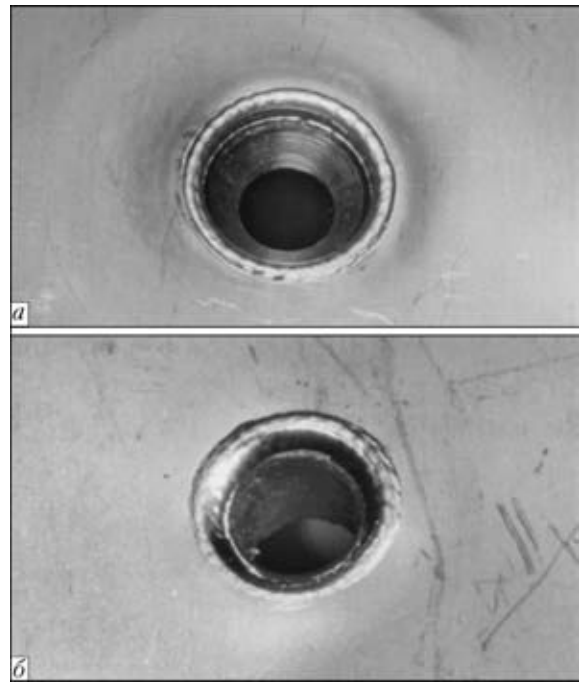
Внешний вид кольцевых швов при сварке отбортовка – тонкая пластина ($\times 4$) на штенгеле (*a*) и ниппеле (*б*)
